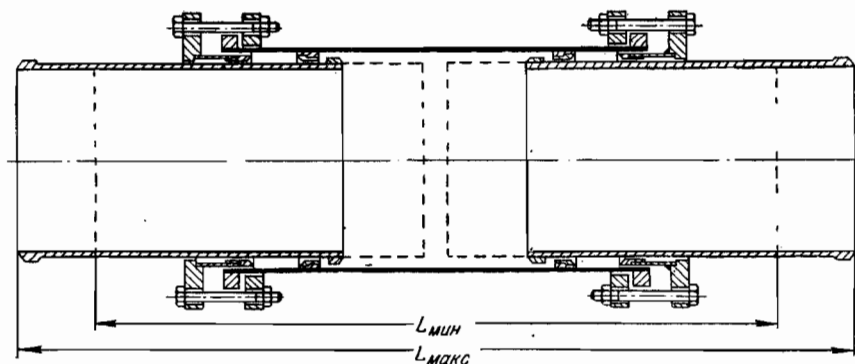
Сдвоенный сальниковый компенсатор сварной конструкции.
